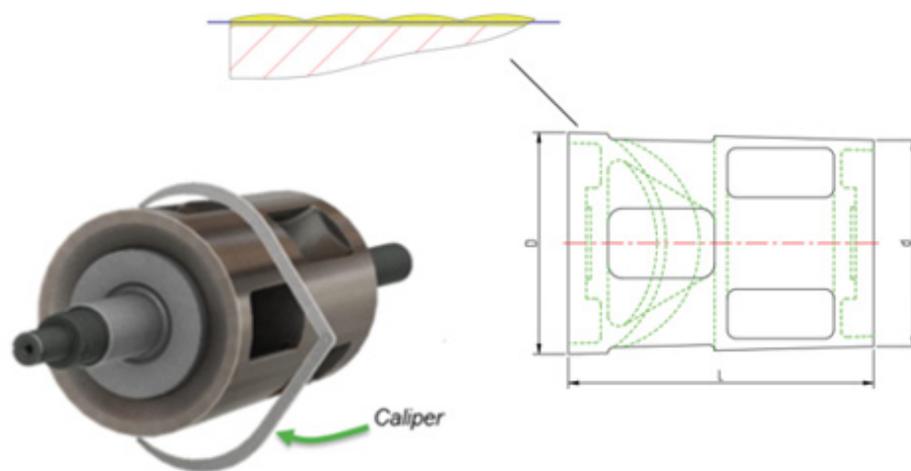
Método Atual de Inspeção e Liberação dos Rotores para a Usinagem
